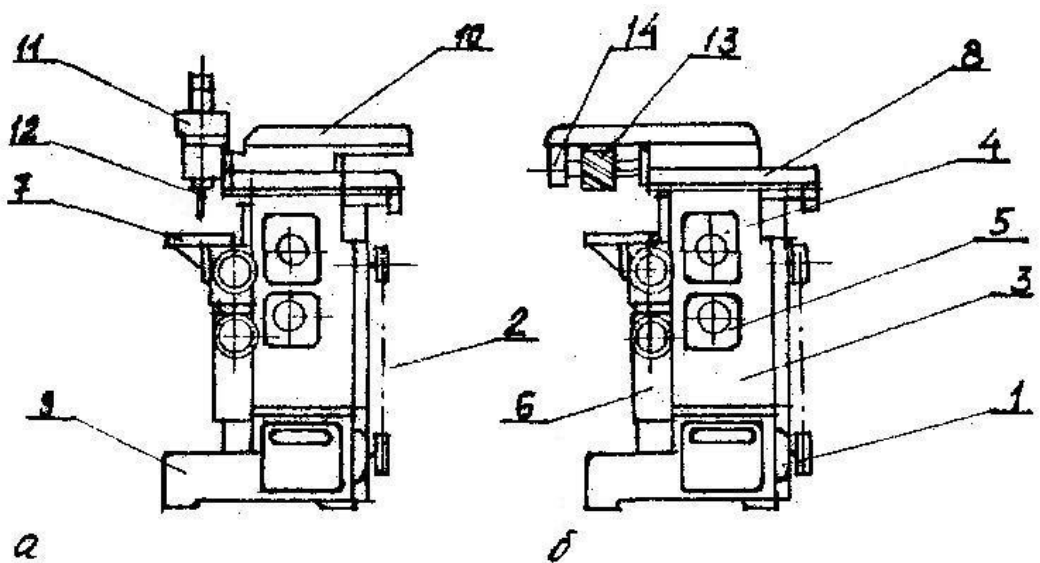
Основні вузли широкоуніверсального фрезерувального верстата
